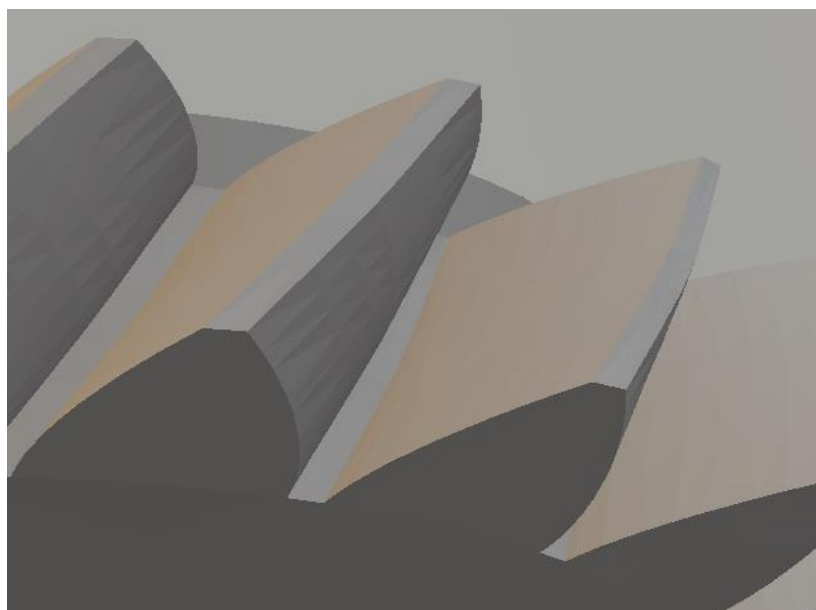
Hueco del engranaje. Fuente: Elaboración propia.
